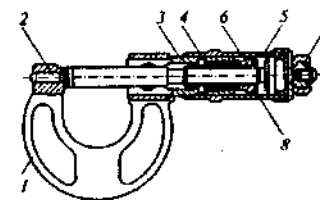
Гладкий микрометр (ГОСТ 6507-90): 1 – корпус; 2 – неподвижная пятка; 3 – стембель; 4 – микрометрический винт; 5 – барабан; 6 – гайка; 7 – устройство стабилизации усилия измерений (трещетка); 8 – контргайка
